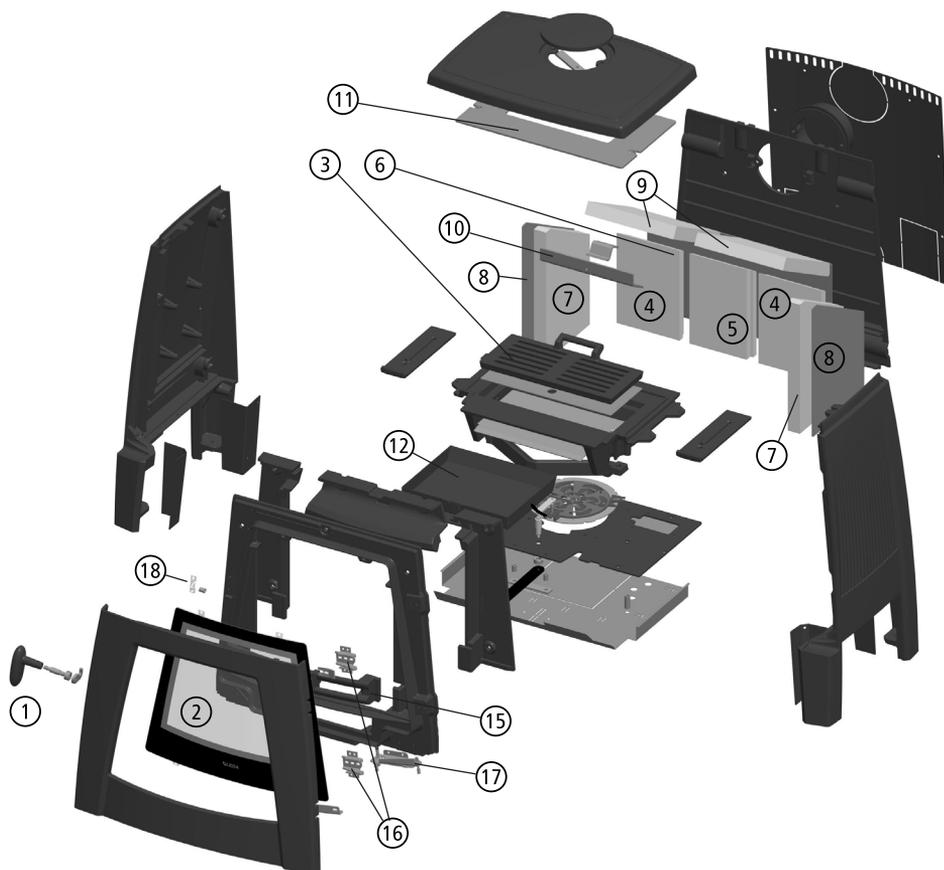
Éclaté : Pièces de rechange de l'APELLA small
